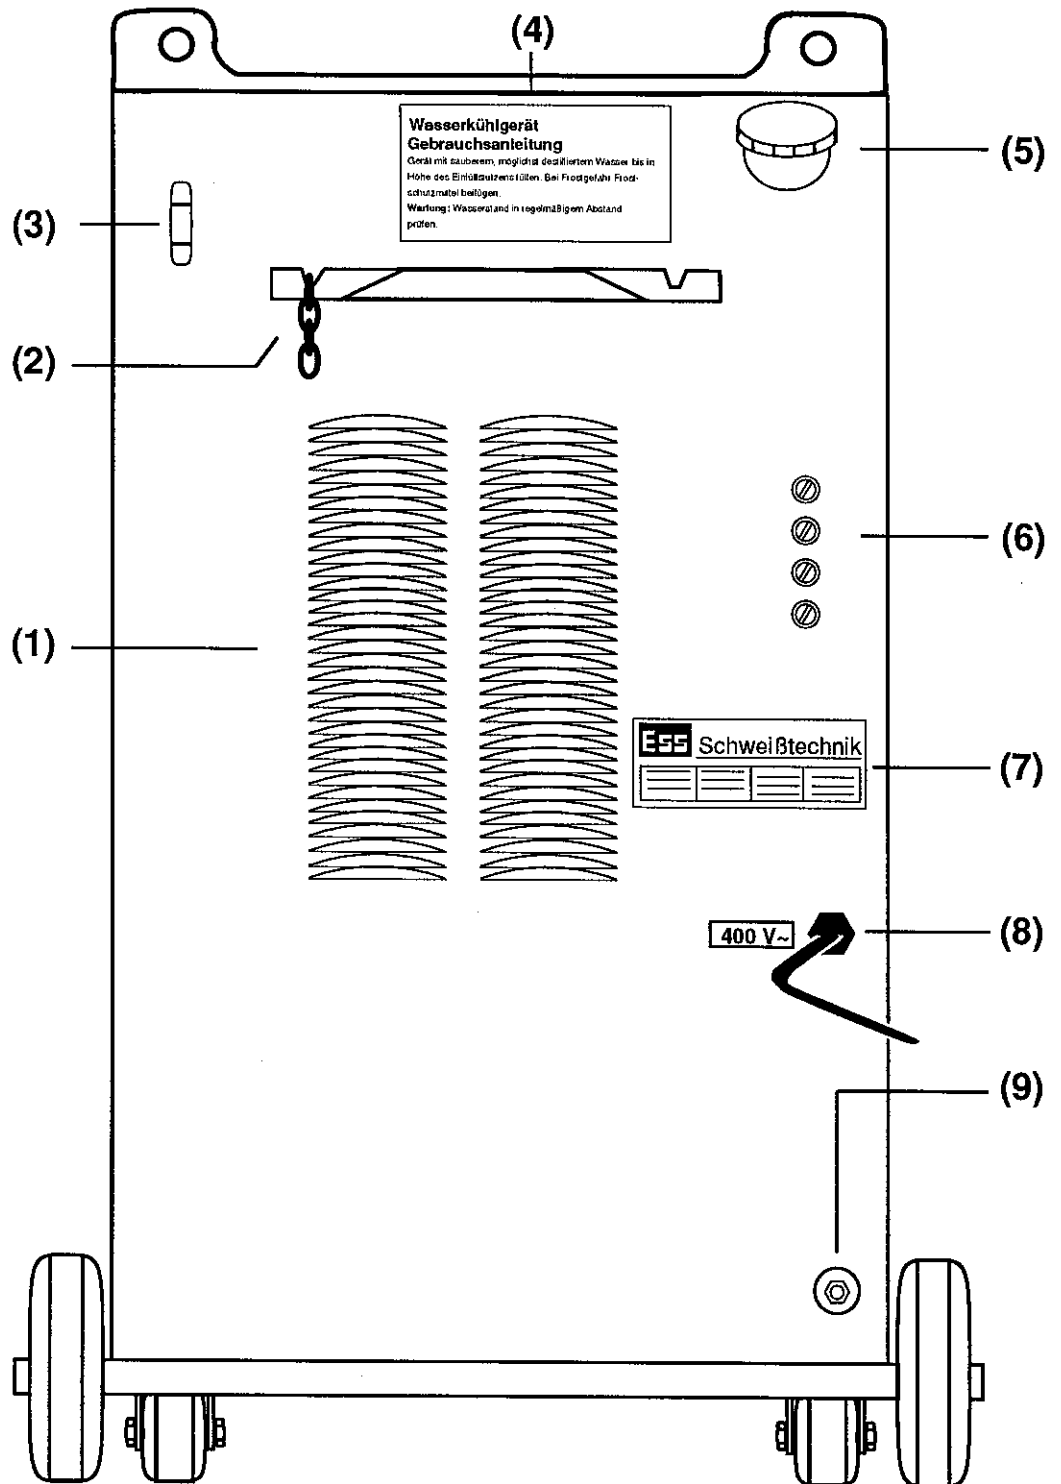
WIG-Schweißstromquelle, Typ Squarearc 250, Rückansicht
